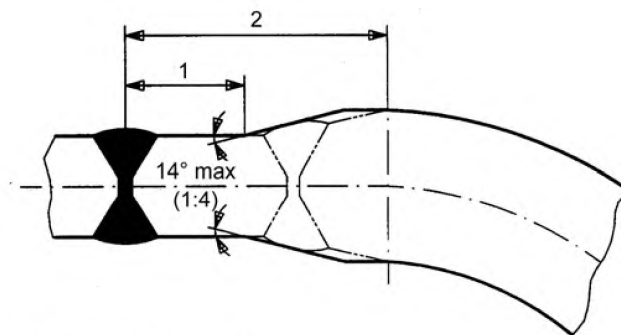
Типовые примеры сварных швов с отбортовкой внутрь кромок днища
